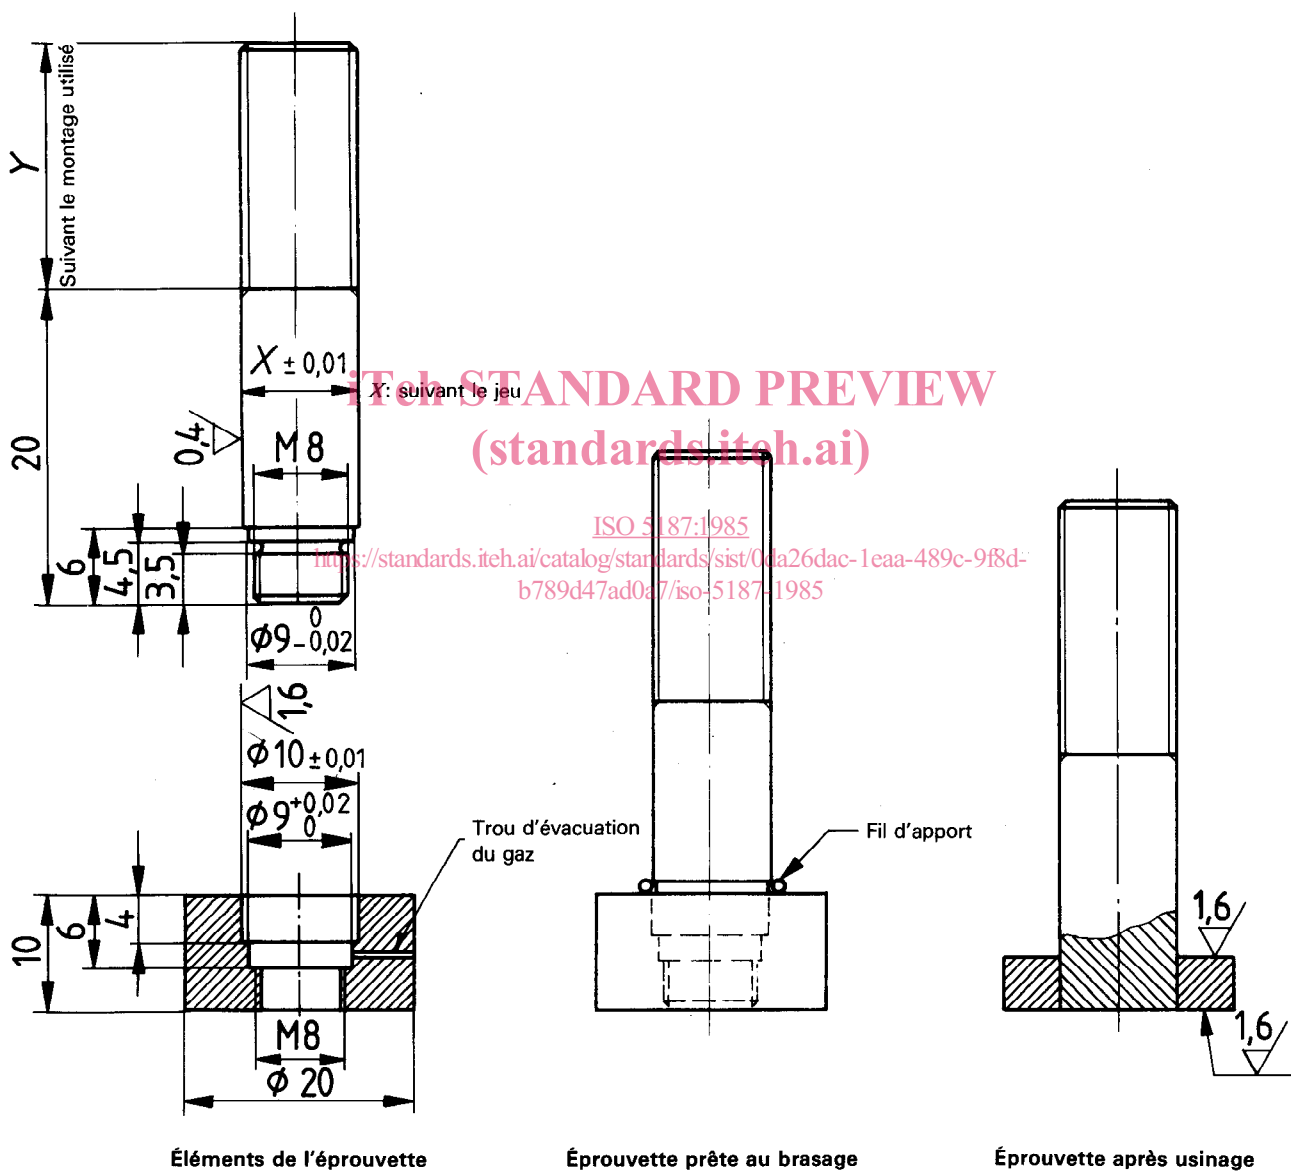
Dimensions de l'éprouvette de cisaillement type II
